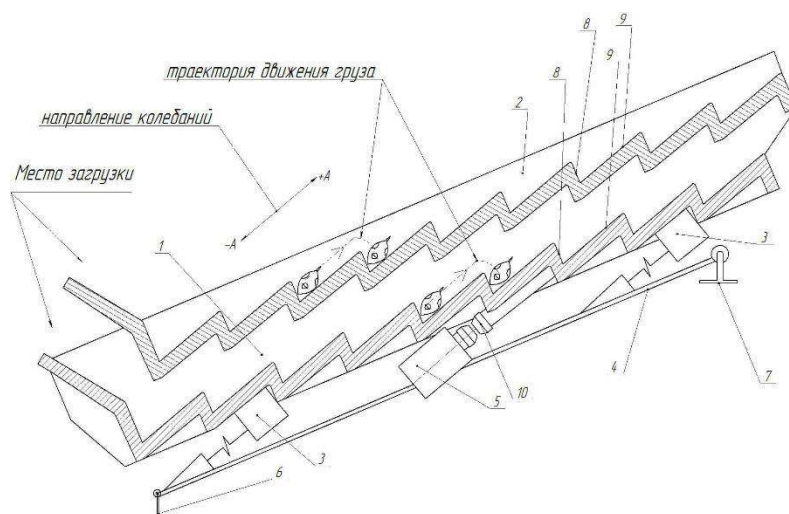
Схема конструкции вибрационного конвейера с двумя ступенчатыми рабочими поверхностями
